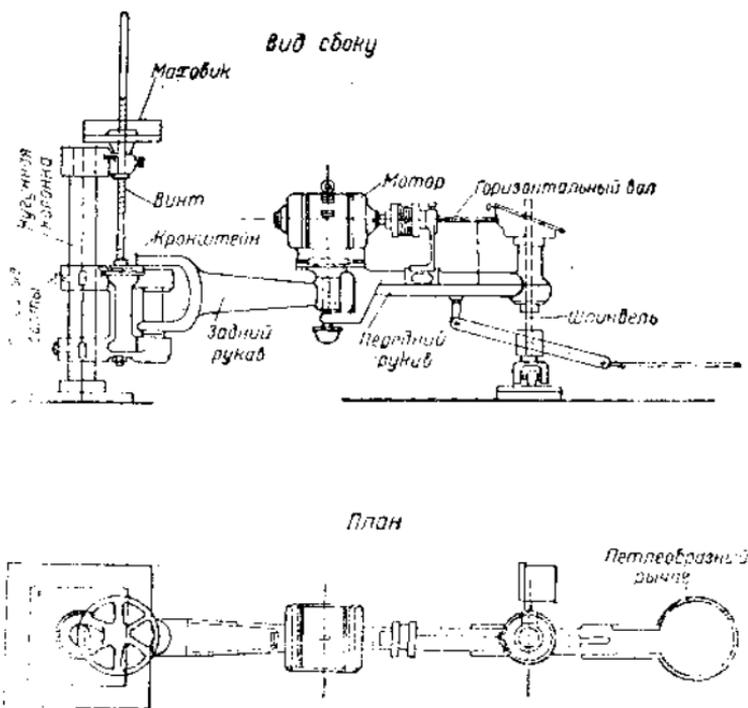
Колонковый шлифовально-полировочный станок (чертеж)
